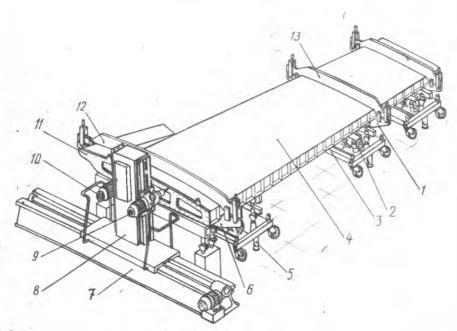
Стенд для разделки фланцевого стика крыда: 1,6 - неподвижные ложементы: 2 - подвижные ложементы: 3 - подвижная тележка: 4 - крыко (ОЧК); 5 - стойка; 7 - станина; 8 - колонна; 9 - свержильная головка; 10 - фрезерная головка; 11 - плита-кондуктор; 12,13 - рубильники
